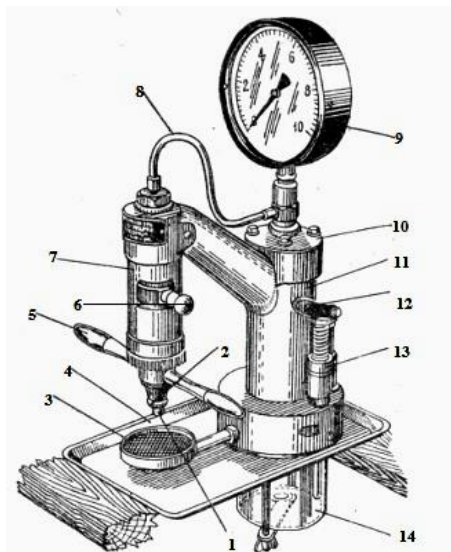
Прибор КИ-1086 для испытания нагнетательных клапанов: 1 – трещотка; 2 – винт микрометрический; 3 – воронка приемная с фильтром; 4 – противень; 5 – рукоятка поджима; 6 – рукоятка втулки; 7 – устройство для крепления нагнетательного клапана; 8 – трубопровод; 9 – манометр; 10 – крышка; 11 – гидроаккумулятор; 12 – рукоятка нагнетательного насоса; 13 – нагнетательный насос, 14 – емкость топливная
